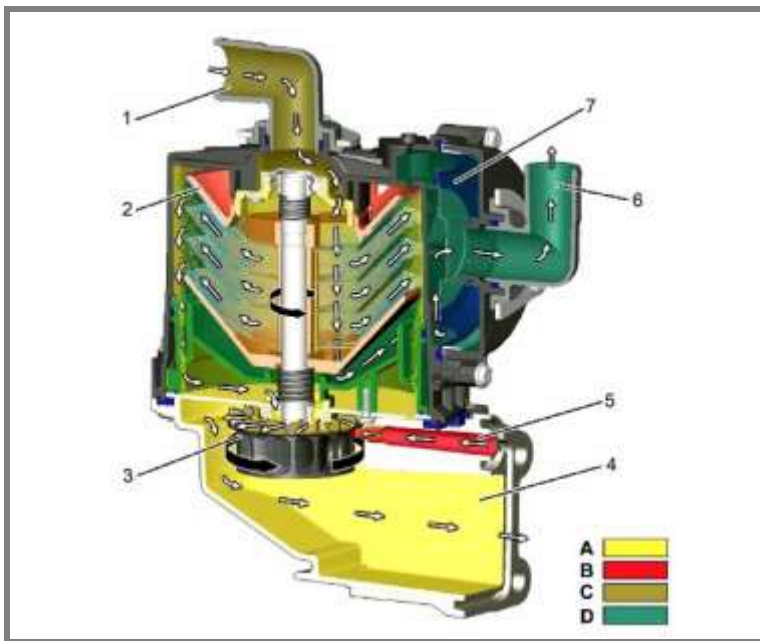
Маслоочисник дизеля FRT вантажного автомобіля: 1 – вхідний патрубок (вхід картерних газів); 2 – центрифуга; 3 – приводне колесо центрифуги; 4 – злив моторного масла; 5 – масляний канал високого тиску; 6 – вихідний патрубок (вихід картерних газів); 7 – клапан регулювання тиску; А – моторне масло; В – моторне масло (для привода центрифуги); С – картерні гази (з моторним маслом); D – картерні гази (очищені)
